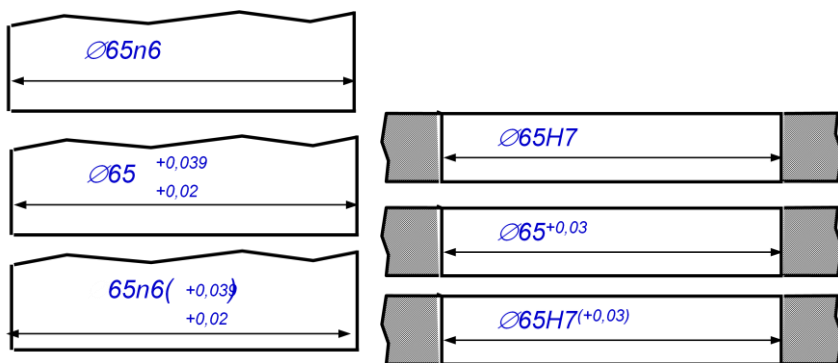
Возможные обозначения поля допуска на диаметр вала и отверстия.
